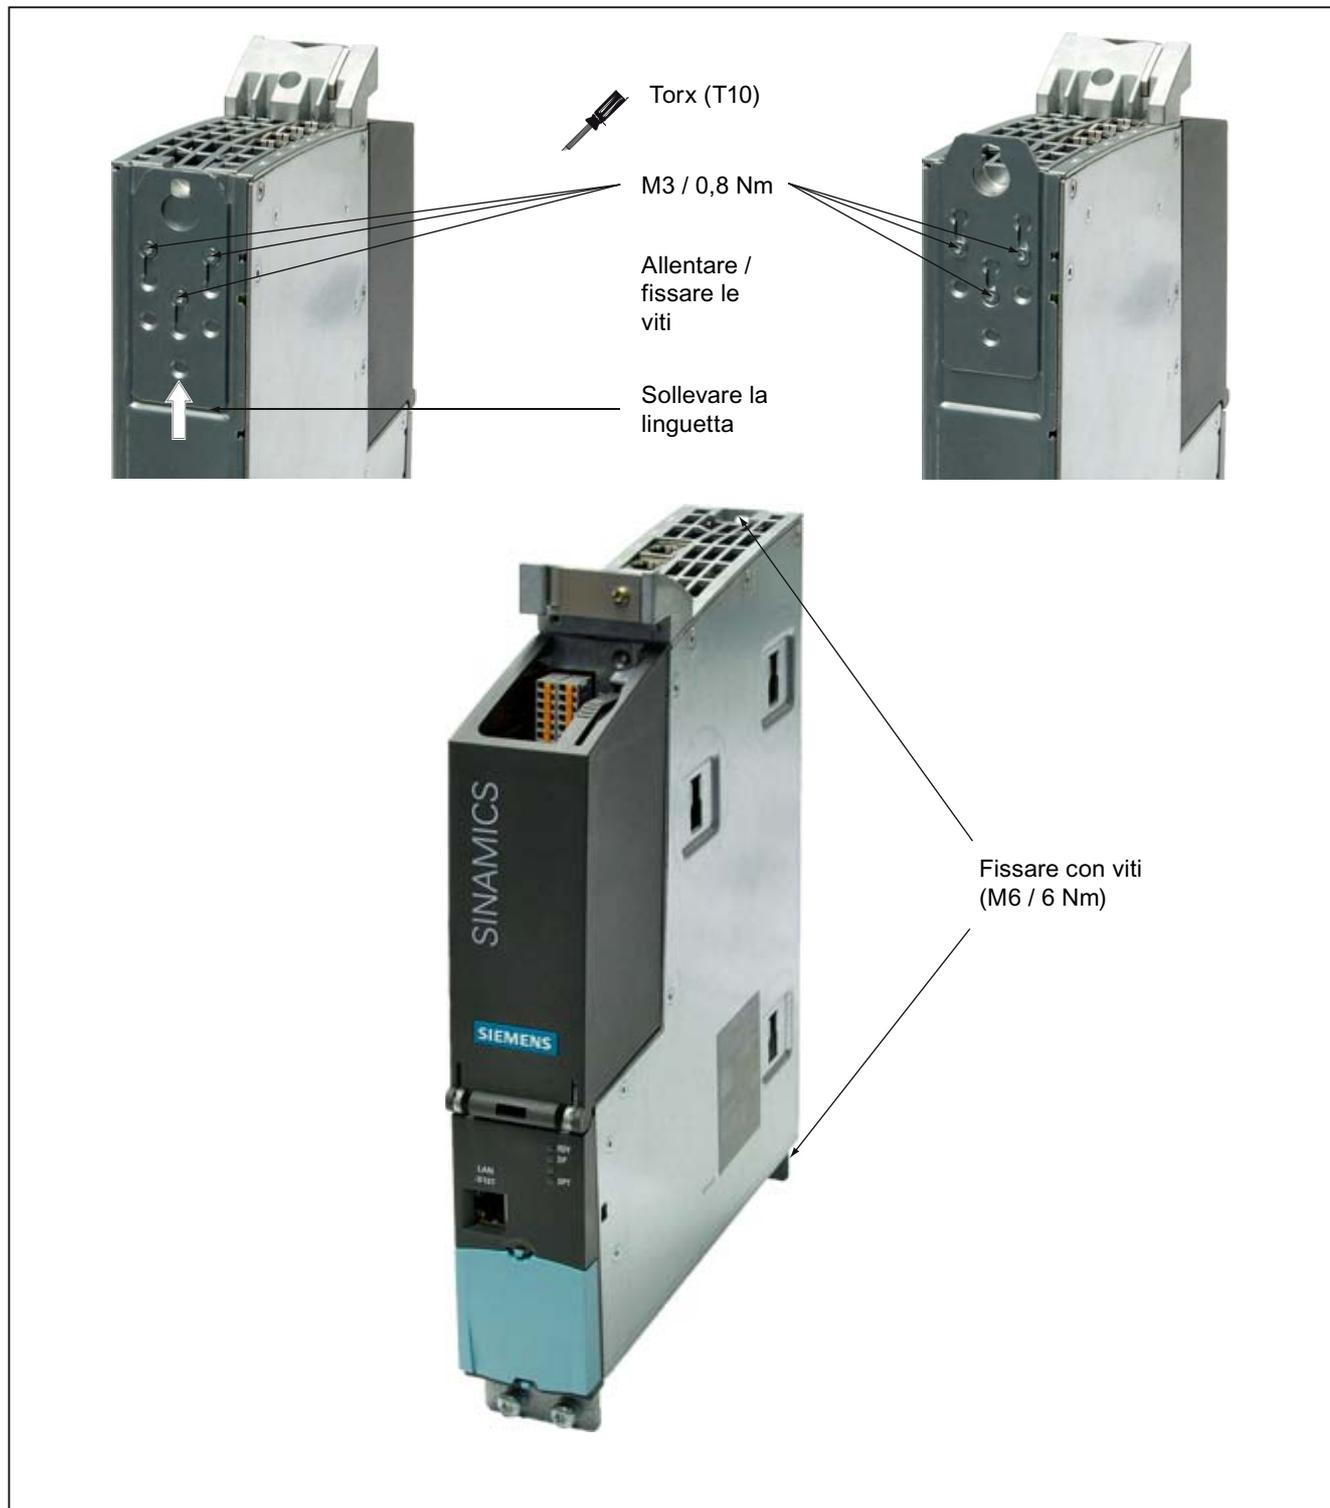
Montaggio della CU320-2 DP su una superficie di montaggio
